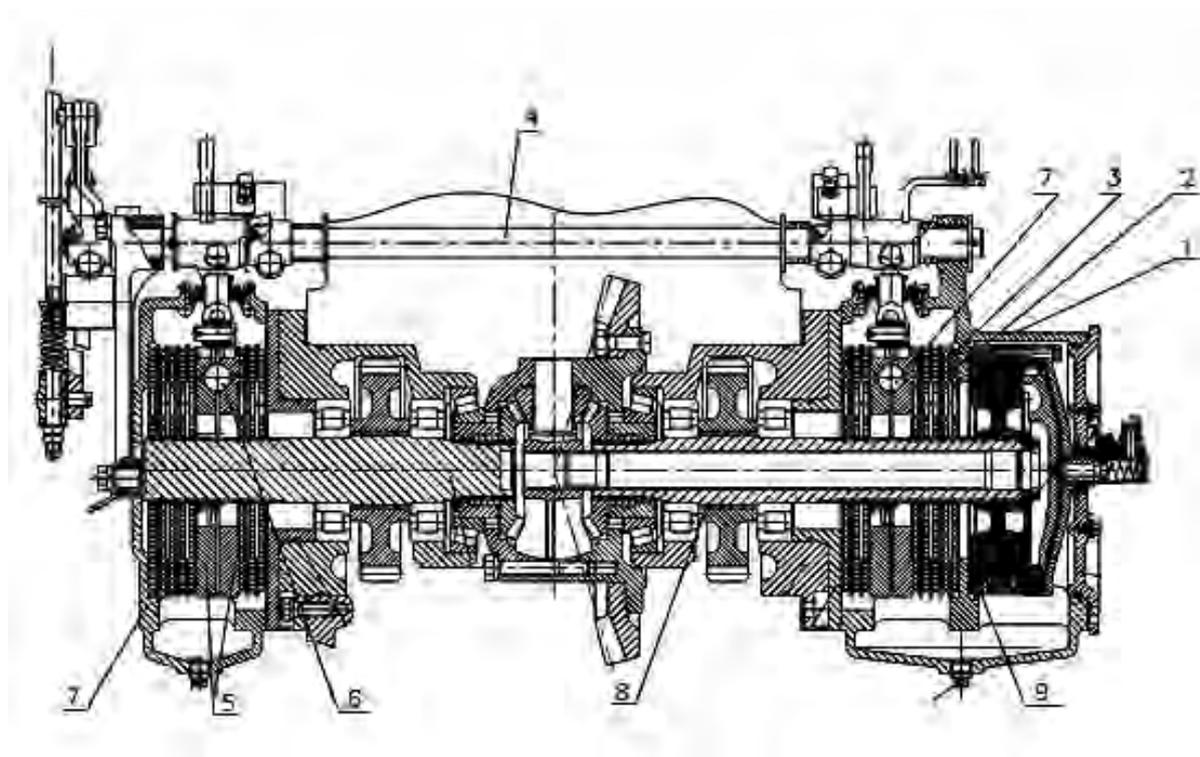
Рабочие тормоза трактора «Беларус-1523»: 1 – корпус тормоза; 2 – диск фрикционный; 3 – диск промежуточный; 4 – валик педалей; 5 – диск нажимной; 6 – шарик; 7 – корпус тормоза; 8 – ведущая шестерня конечной передачи; 9 – муфта блокировки дифференциала
